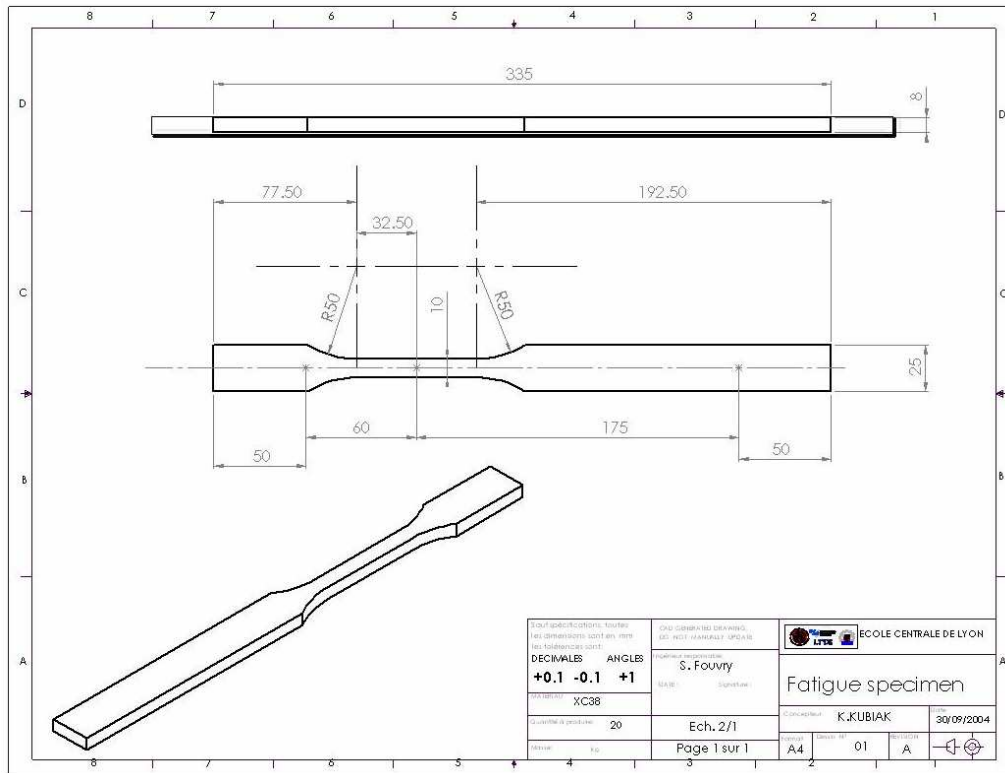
Dessin d'éprouvette Fretting Fatigue
